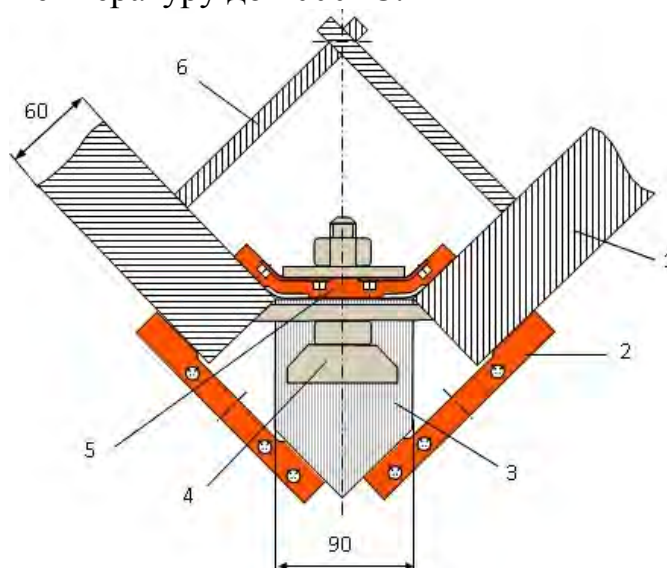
Схема крепления медной водоохлаждаемой накладки на поясах строительной колонны для формирования обратной стороны сварных швов: 1 – пояс колонны; 2 – наружная формирующая накладка; 3 – привариваемый элемент усиления; 4 – прижимное устройство; 5 – формирующая накладка обратной стороны стыка; 6 – ребро жесткости.
